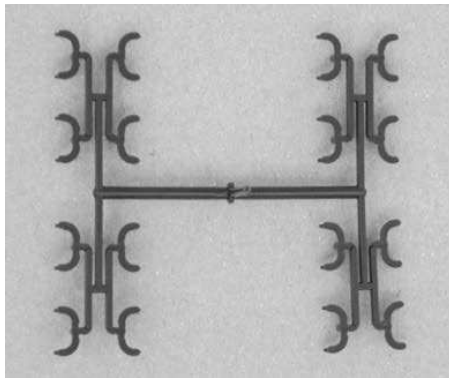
Beispiel für einen mechanisch ausbalancierten Kaltkanalanguss
